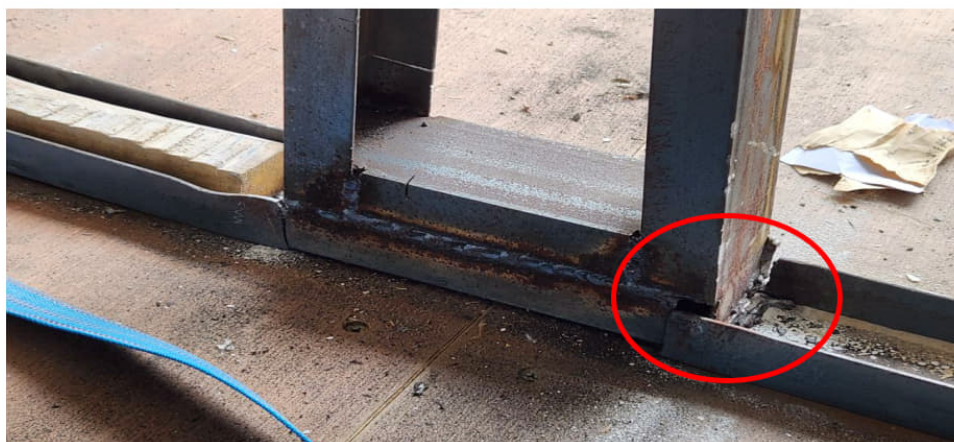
Inclinaison vers la droite des cadres verticaux du support de type A. (Source CNESST).
